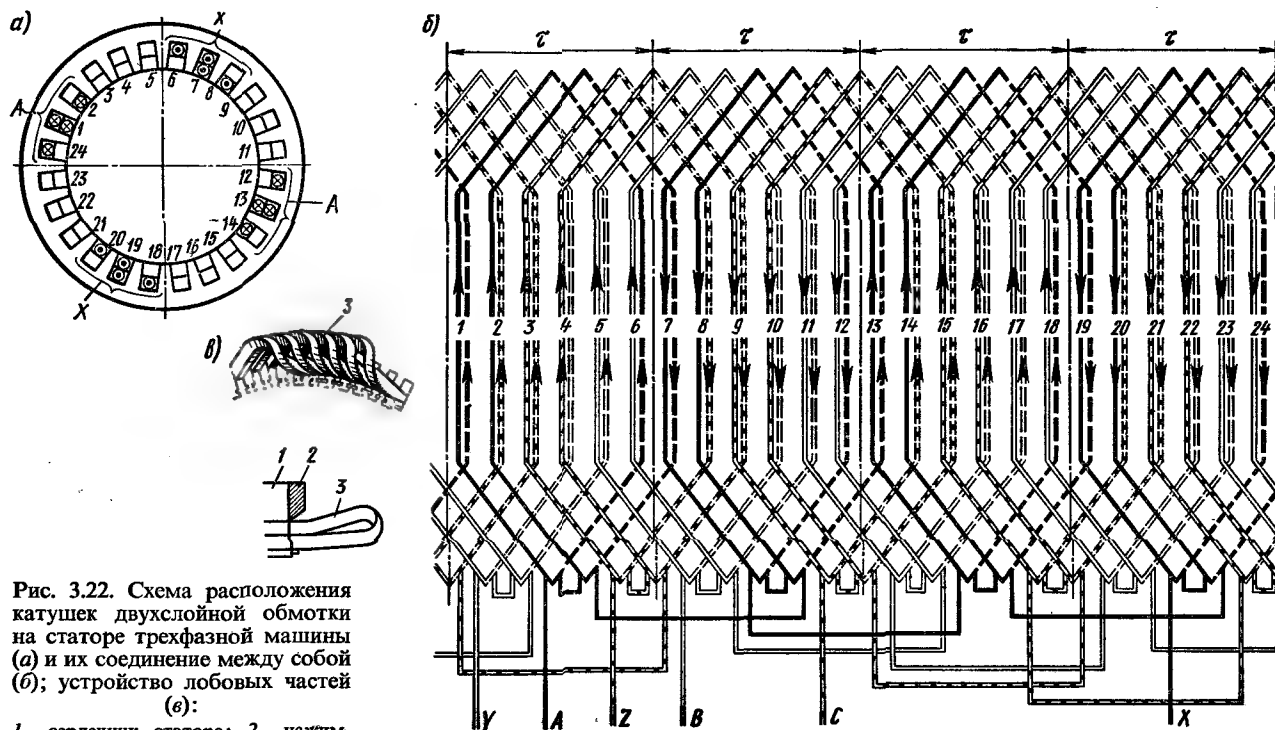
Схема расположения катушек двухслойной обмотки на статоре трехфазной машины (а) и их соединение между собой (б); устройство лобовых частей (в):
